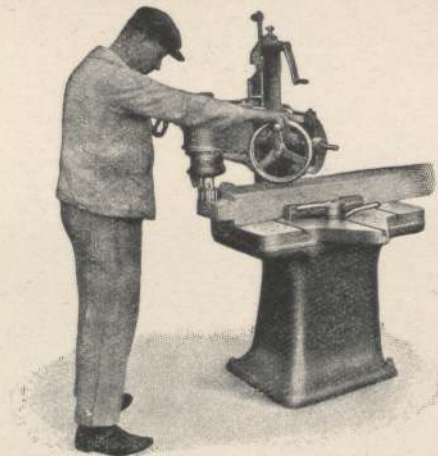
Dieselbe Maschine beim Bearbeiten von Kanthölzern.
